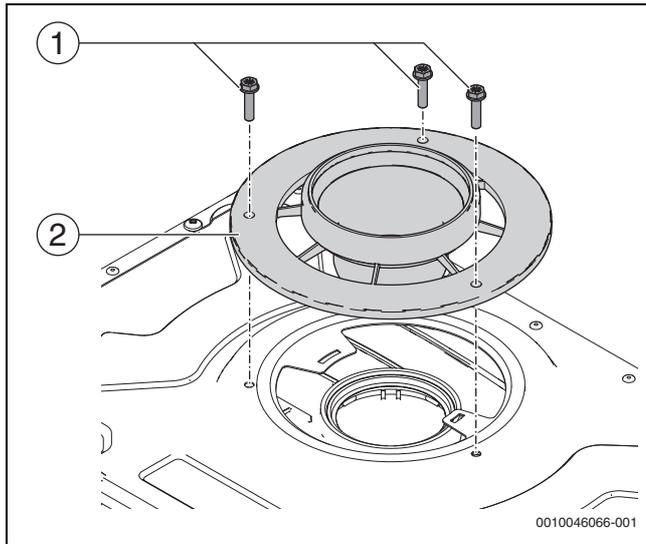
Monter le set du conduit de fumées et l'adaptateur du conduit de fumées
